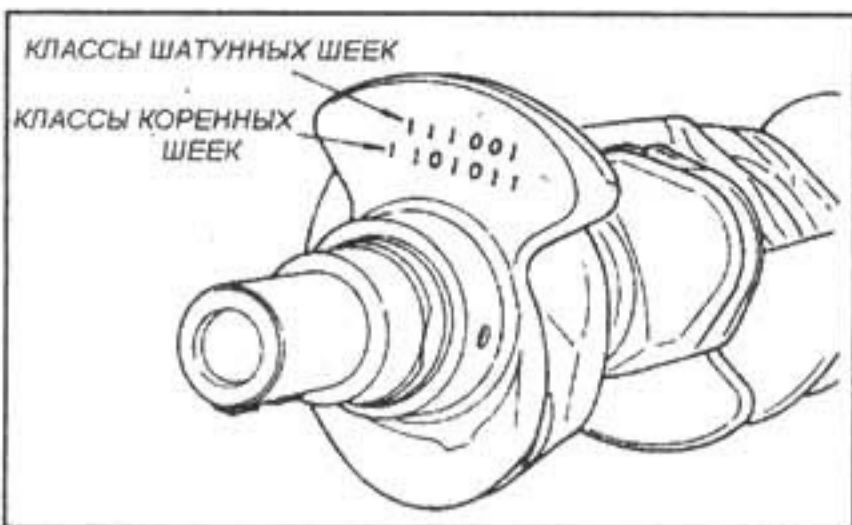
Маркировка коленвала двигателя RD28T.
